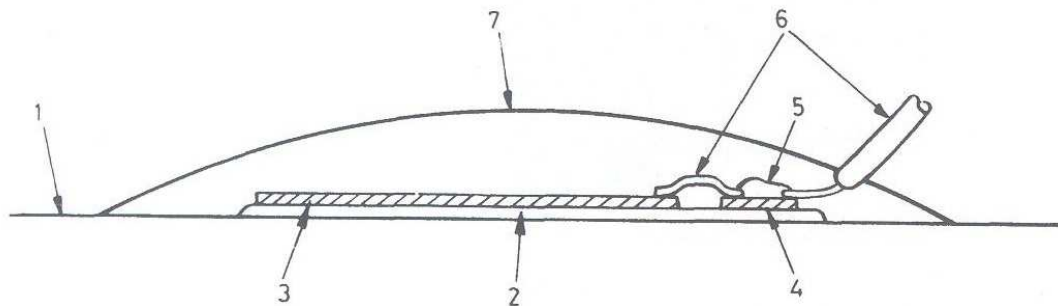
Montaje de la galga. 1 Sustrato donde se monta. 2 adhesivo. 3 Galga. 4 terminales (pads) para soldar. 5 soldadura. 6 hilos de conexión. 7 aislamiento protector.
